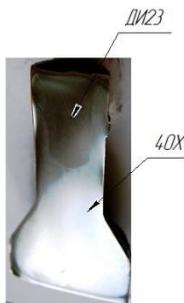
Фото продольного шлифа биметаллической детали типа «Выталкиватель»
